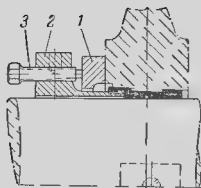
Приспособление для вытаскивания конических втулок, крепящих диски.
